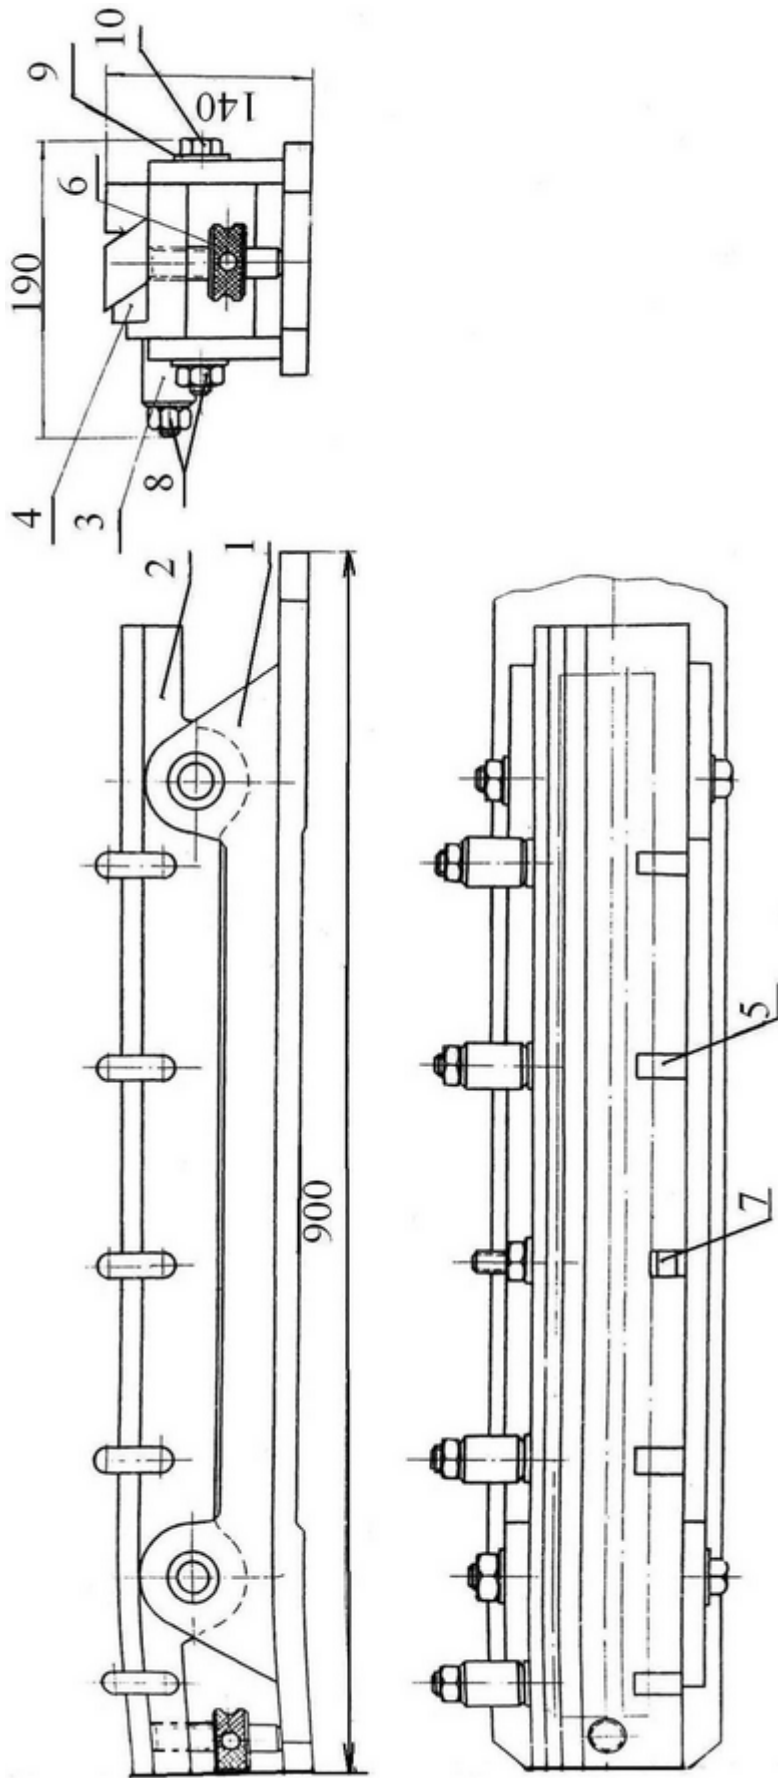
Приспособление для строгания и шлифования клиньев СД 7222 – 4001
